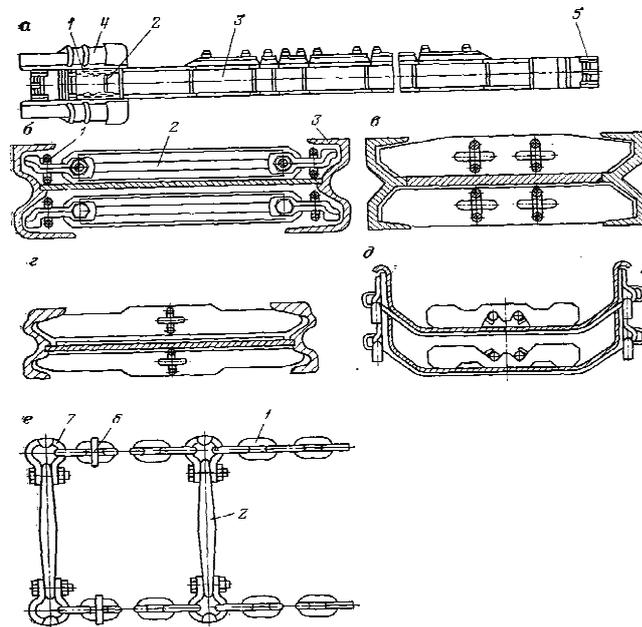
Скребковый конвейер (а), конструкции рештачного става (б-д) и тяговые цепи со скребками (е)
